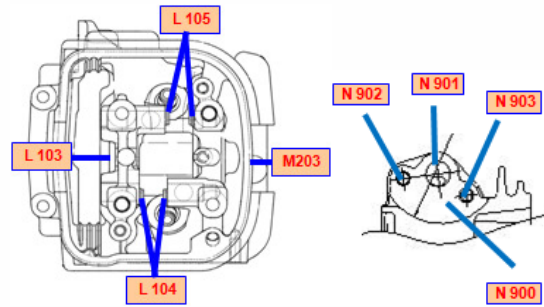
Proses OP 20 *Cylinder Head Machining
